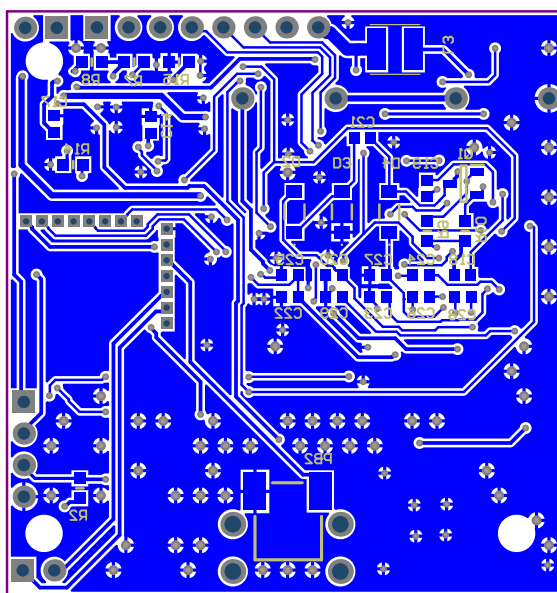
Capas Bottom y Bottom Overlay de la PCB diseñada.
